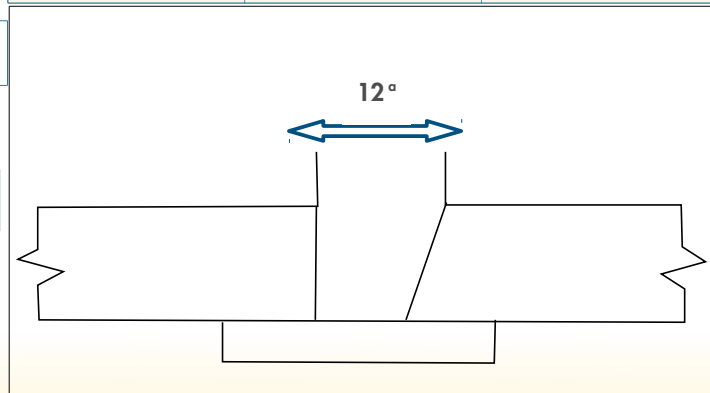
pièce d'épreuve combinée pour la soudure d'angle et la soudure bout à bout. Il faut noter que dans ce cas, on utilise un support à l'envers. La qualification n'est donc valable que pour un joint bout à bout avec support à l'envers
